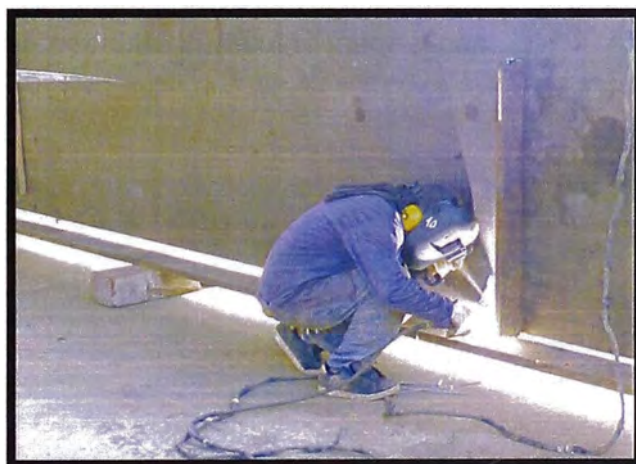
Soldado de las piezas de acero.
